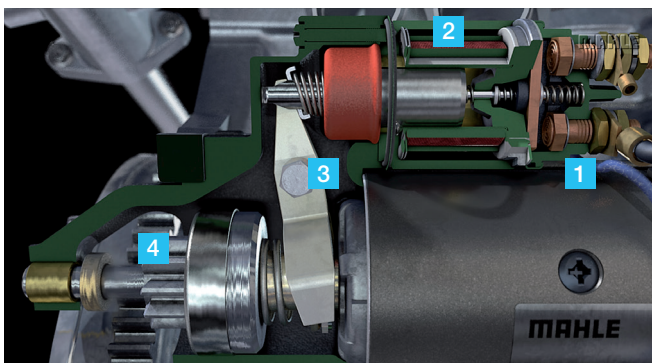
Sección del motor de arranque con puente de contacto (1), solenoide (2), palanca de embrague (3) y piñón con embrague de rueda libre (4)
